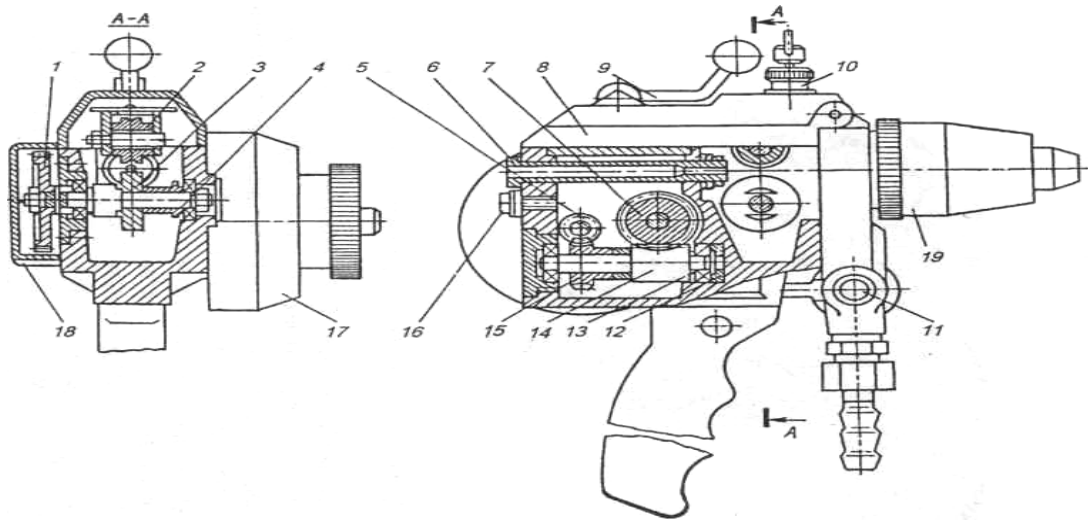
Ручний металізатор МГІ-4 для газополуменевого напилення дротяного матеріалу:
